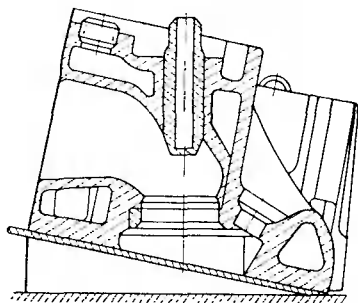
Положение головки блока цилиндров при перепрессовке направляющих втулок клапанов
